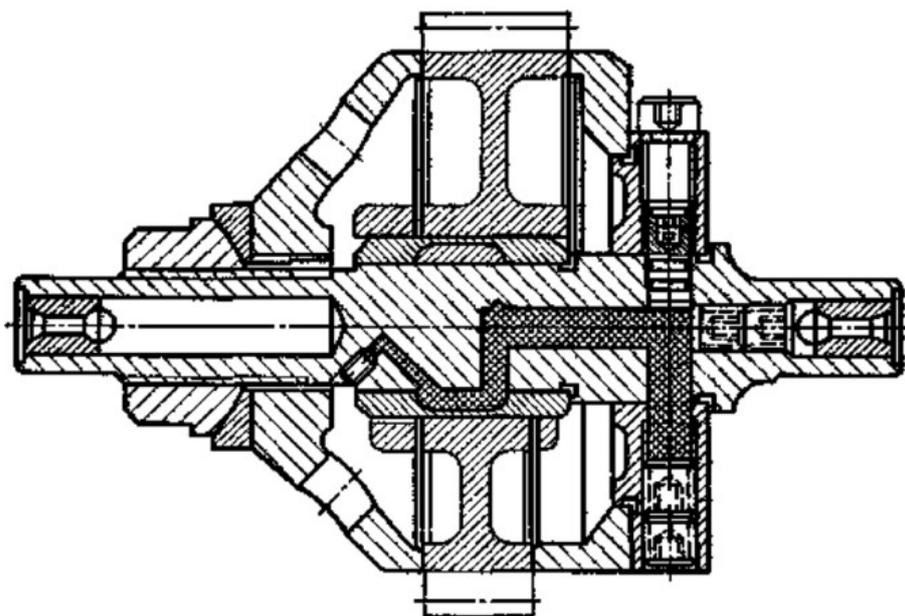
Схема установки колес на зубошеввинговальных станках с горизонтальной осью на разжимной оправке с гидропластом
